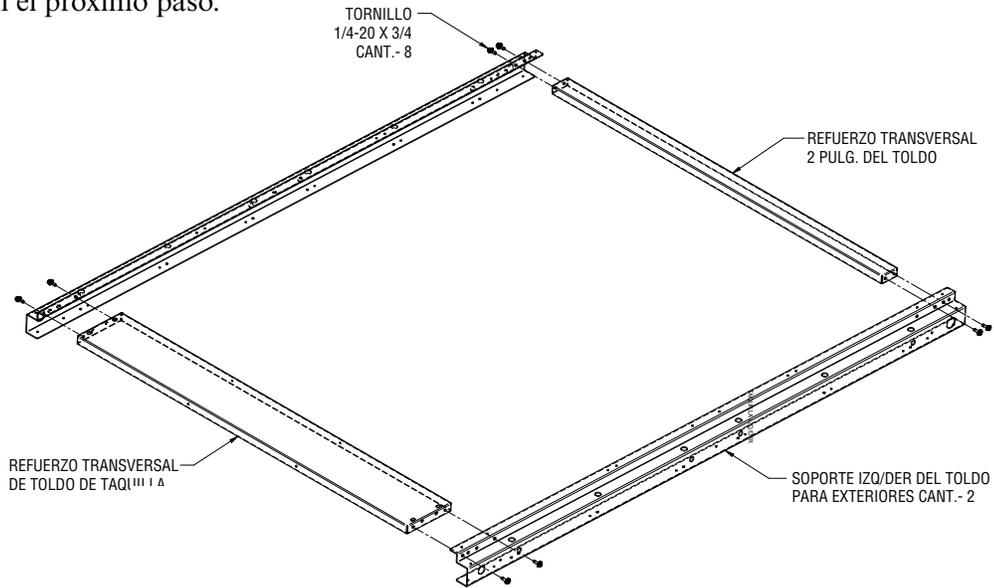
Vista superior del ensamblaje del marco del toldo
